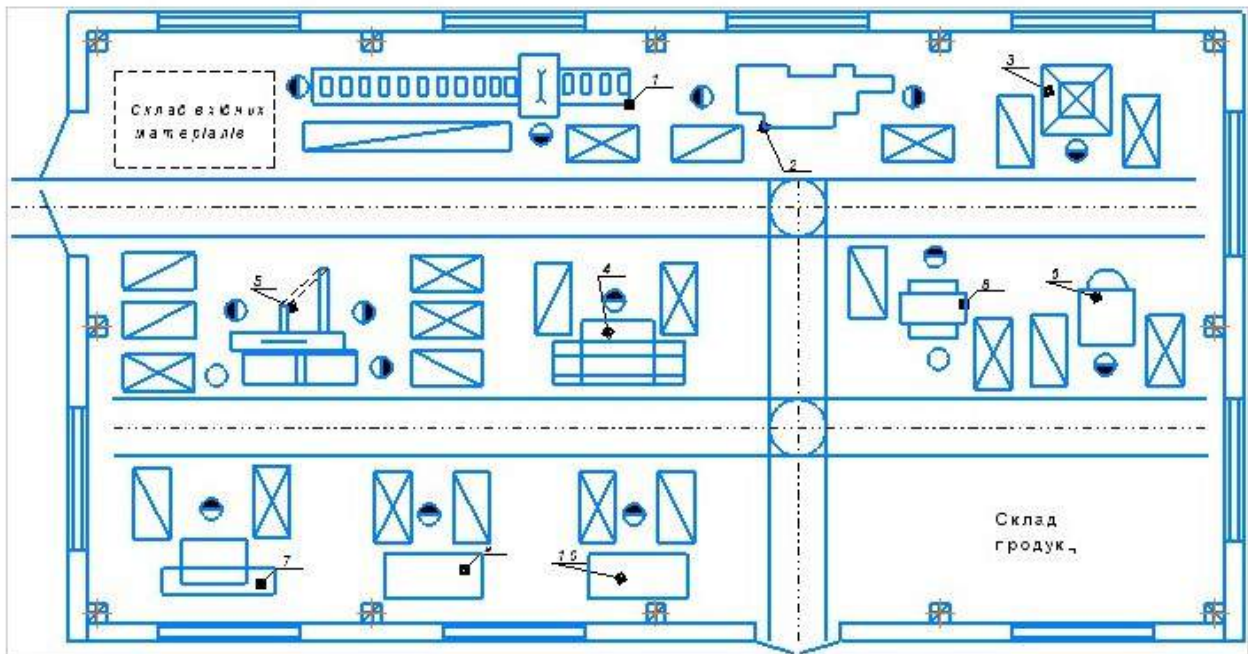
Варіант другий : планування обладнання з виготовлення розсувних дверей рамково-тахлевої конструкції — рамка виготовляється з заготовок, а вставки — зі брусків
